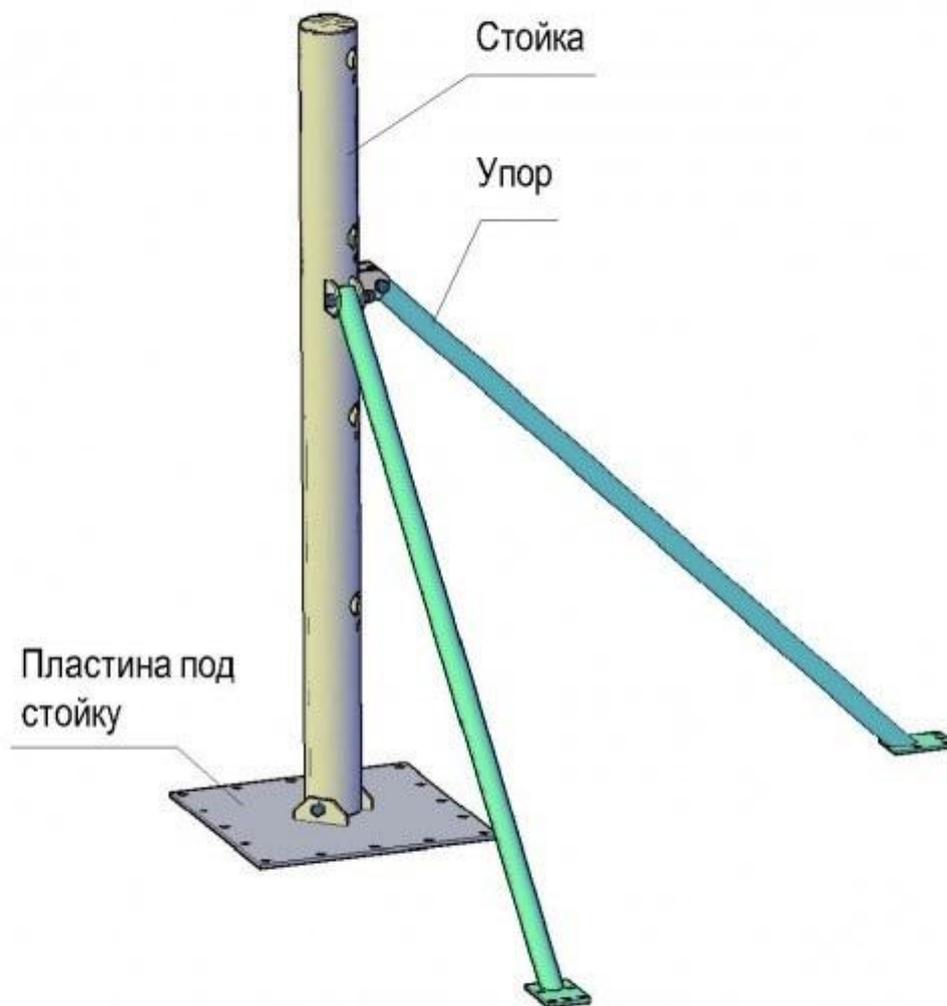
Узел крепления стойки боксерского ринга
